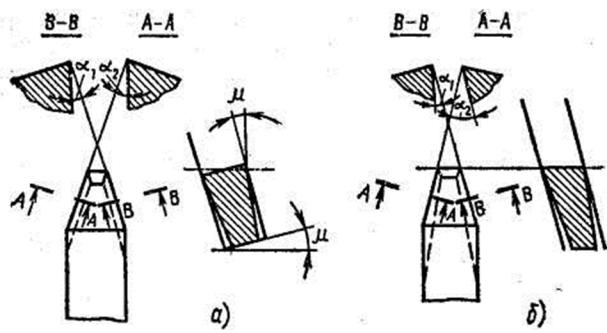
Установка резьбового резца при нарезании трапециoidalной резьбы
